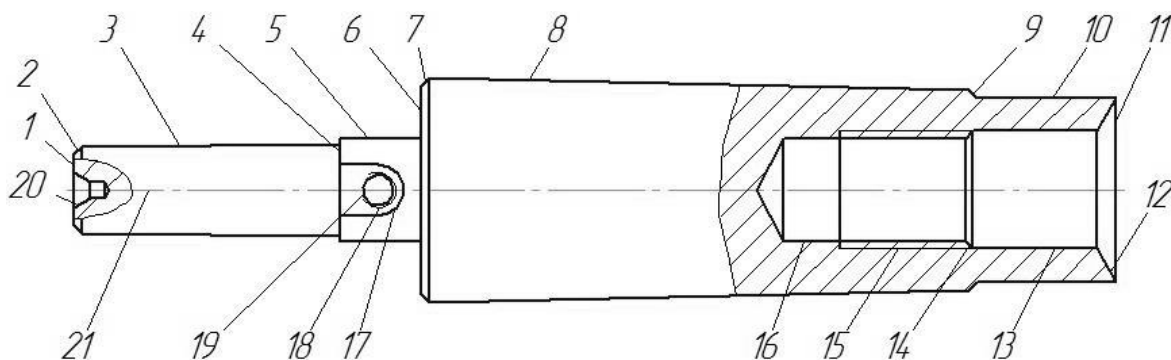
Эскиз корпуса насадного режущего инструмента
